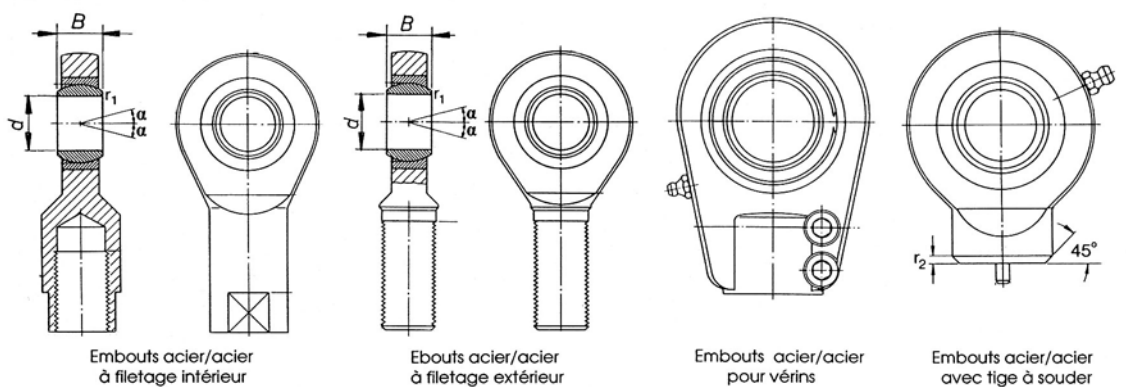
Embouts à rotule de types divers : standard, pour vérins et à souder
